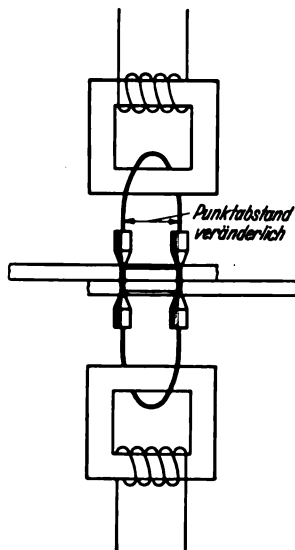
Wirkungsweise der Doppelpunkt-Schweißmaschine.
